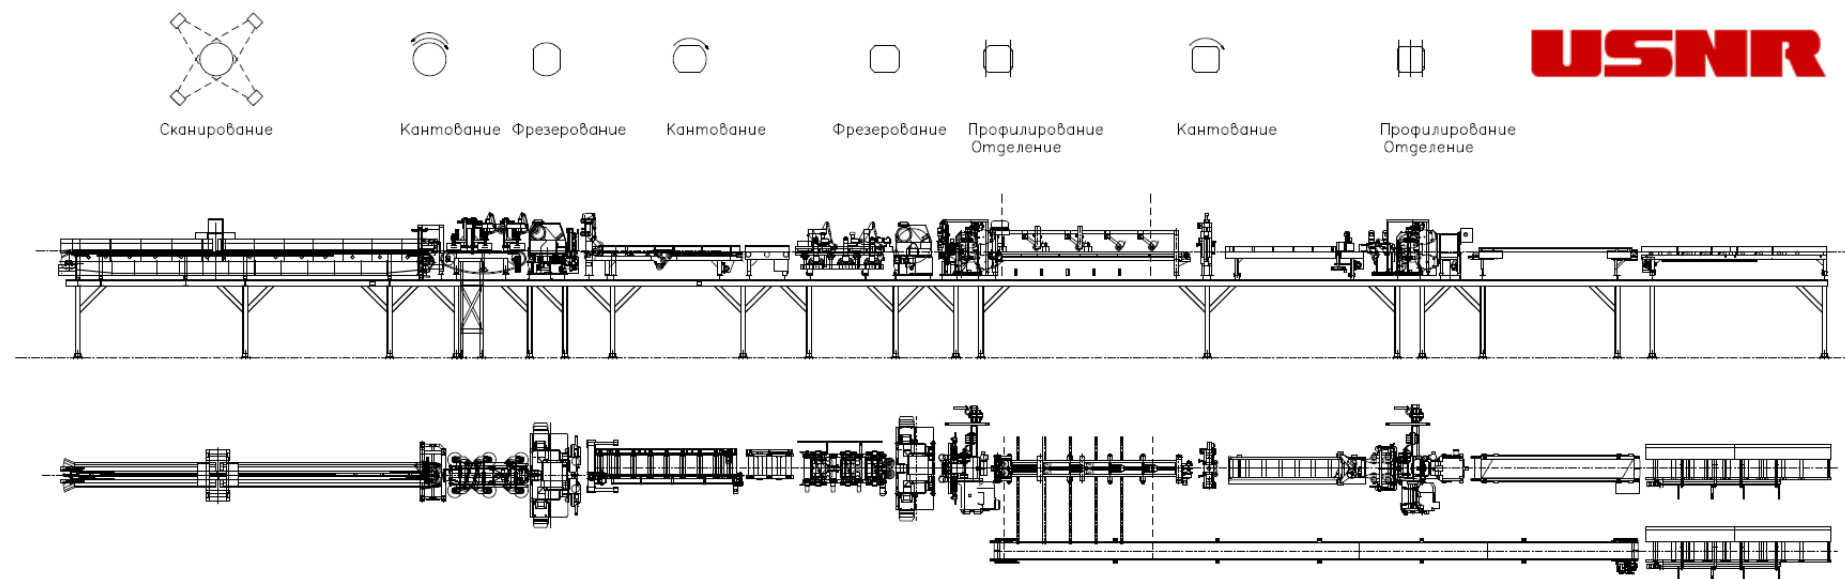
Лесопильная линия на базе фрезерно-профилирующего круглопильного оборудования [10]
